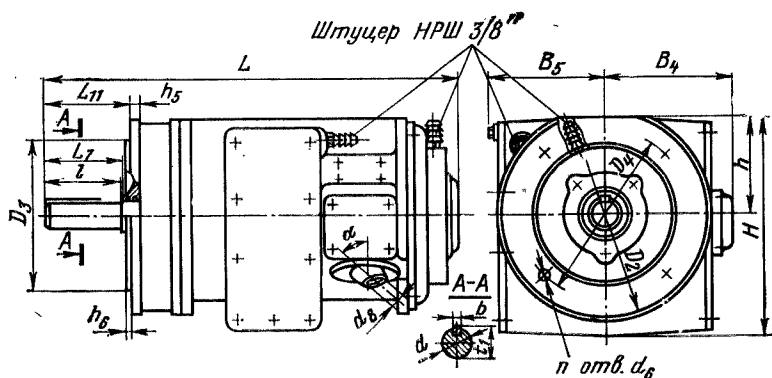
Габаритные и установочные размеры электродвигателей с водяным охлаждением АРФВ 5 и 6-го габаритов.
